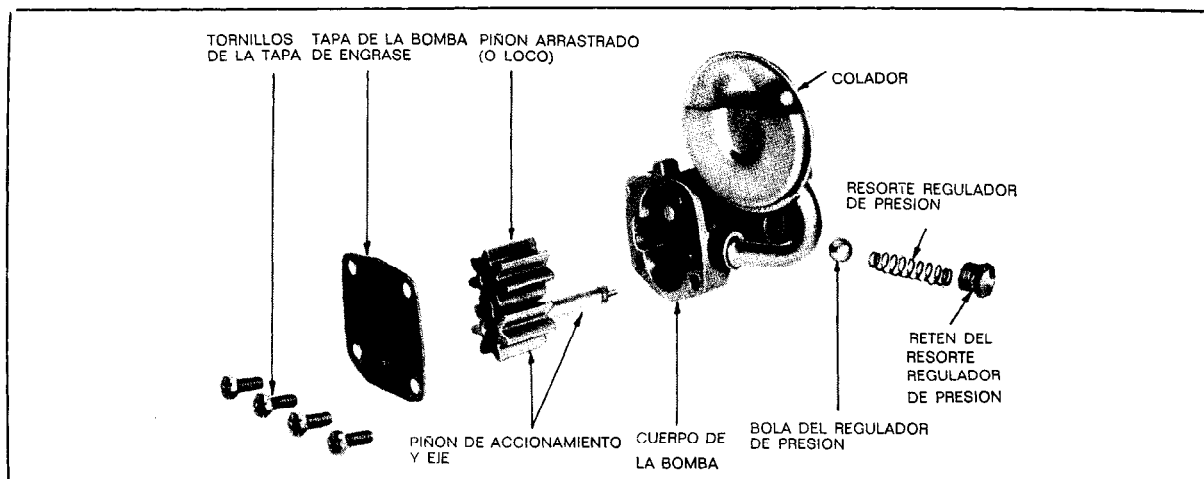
Despiece de una bomba de engrase de engranaes (Pontiac Motor Division of General Motors Corporation).
